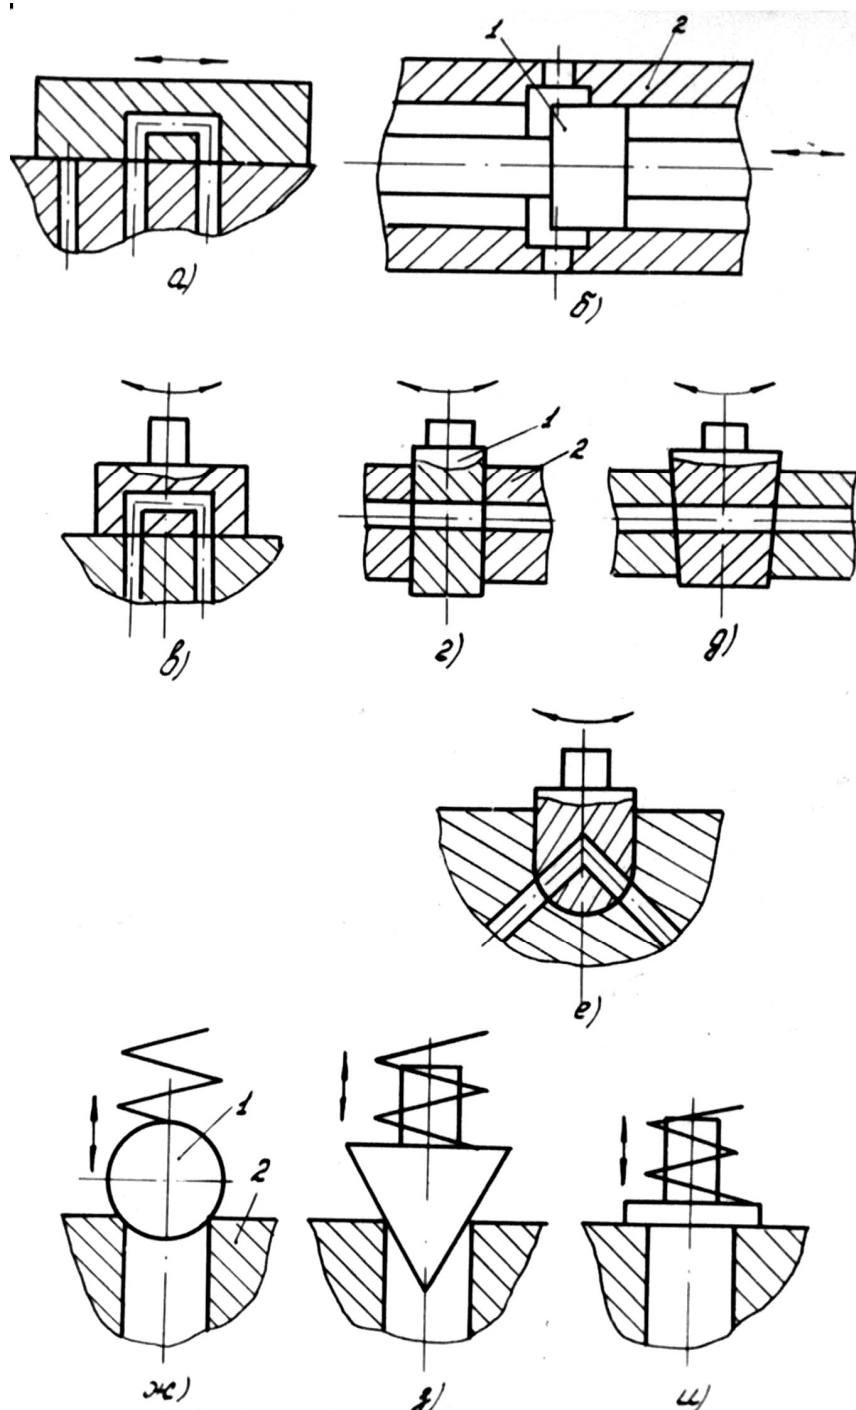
Типы конструкций запорно-регулирующих элементов:
